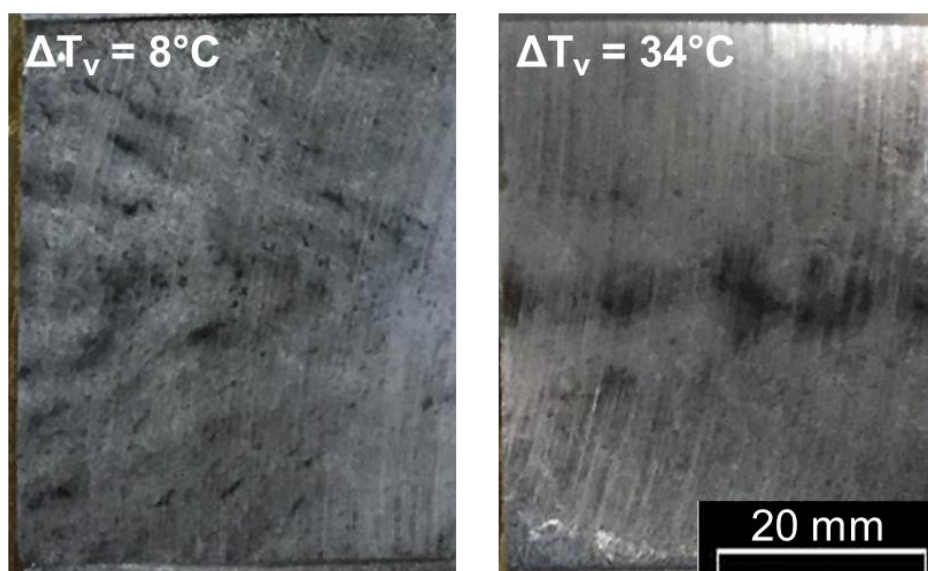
Macroataque para superaquecimentos de 8°C e 34°C.
